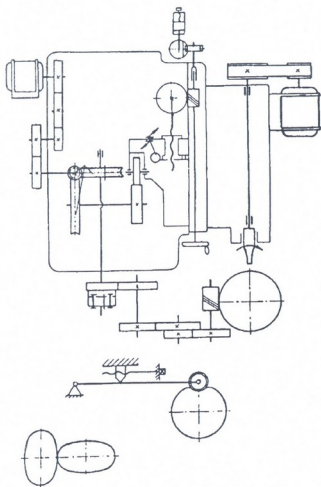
Кинематическая схема зубозакругляющего станка
